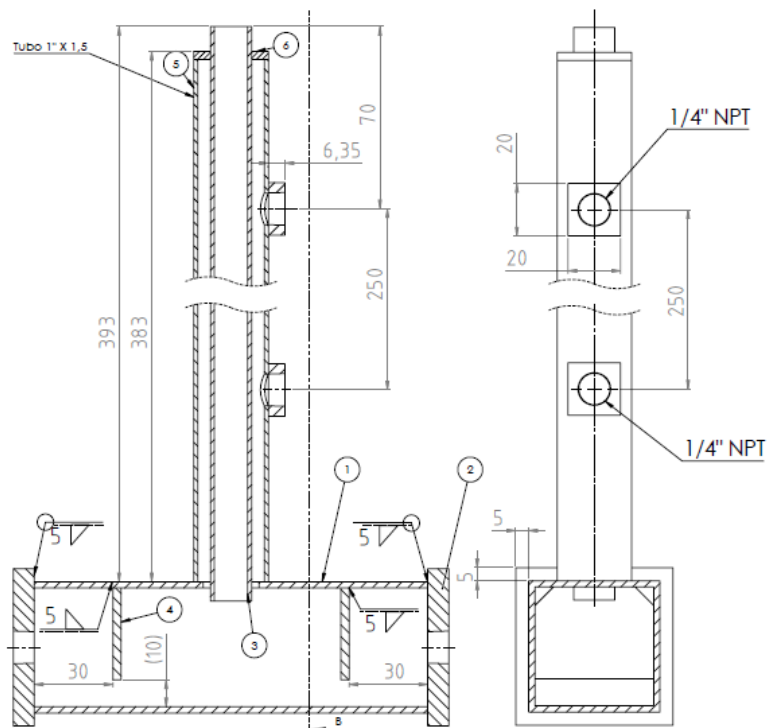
Vista em corte do queimador com câmara de pré-mistura e sistema de refrigeração.
